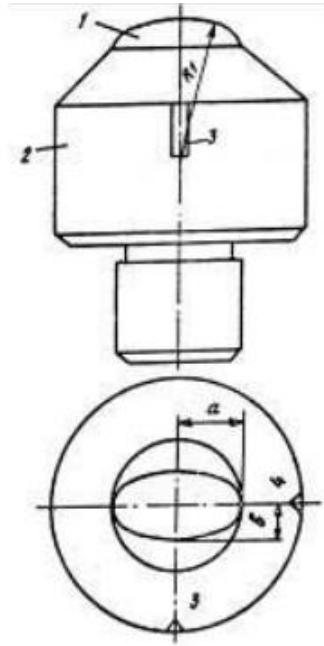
Інструмент з криволінійною формою заточки
